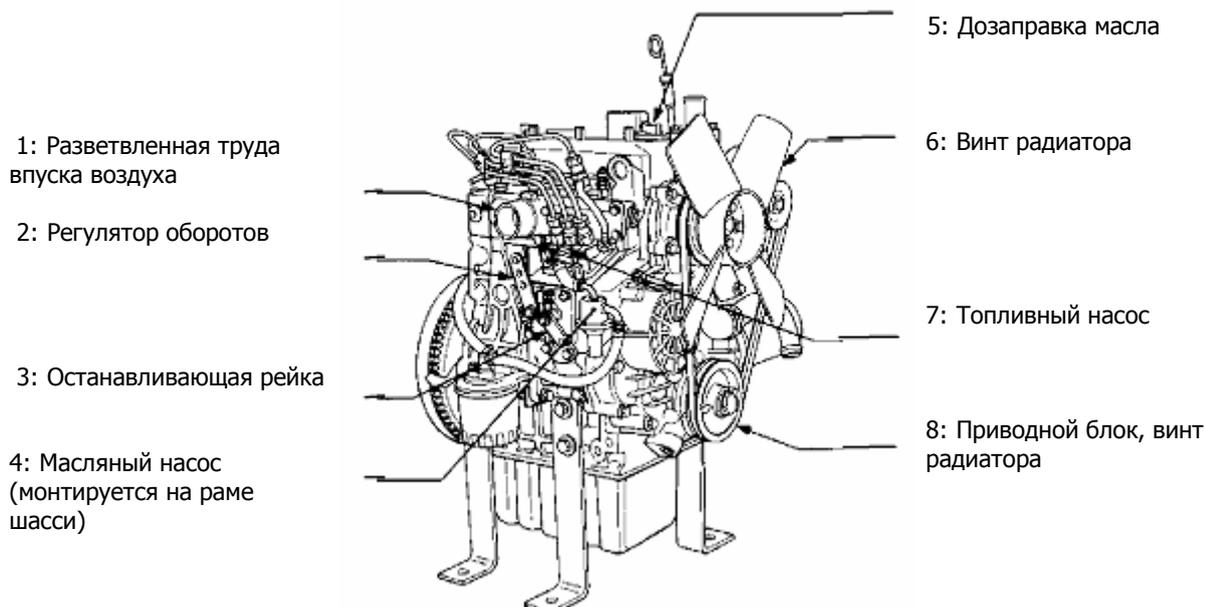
Двигатель «Kubota» D 905-B – вид слева:
